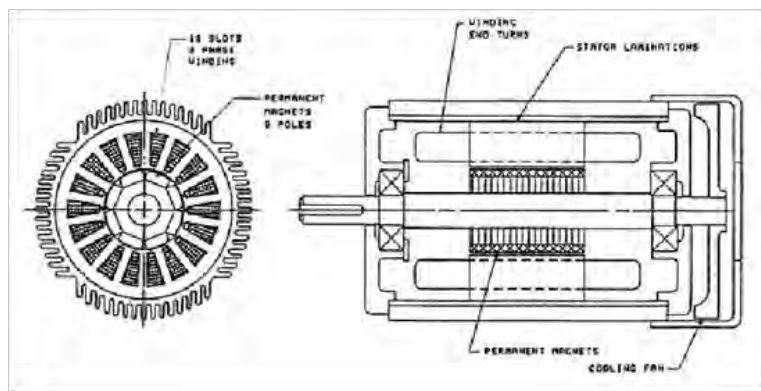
Coupe Machine synchrone (NEMA 184 T)
